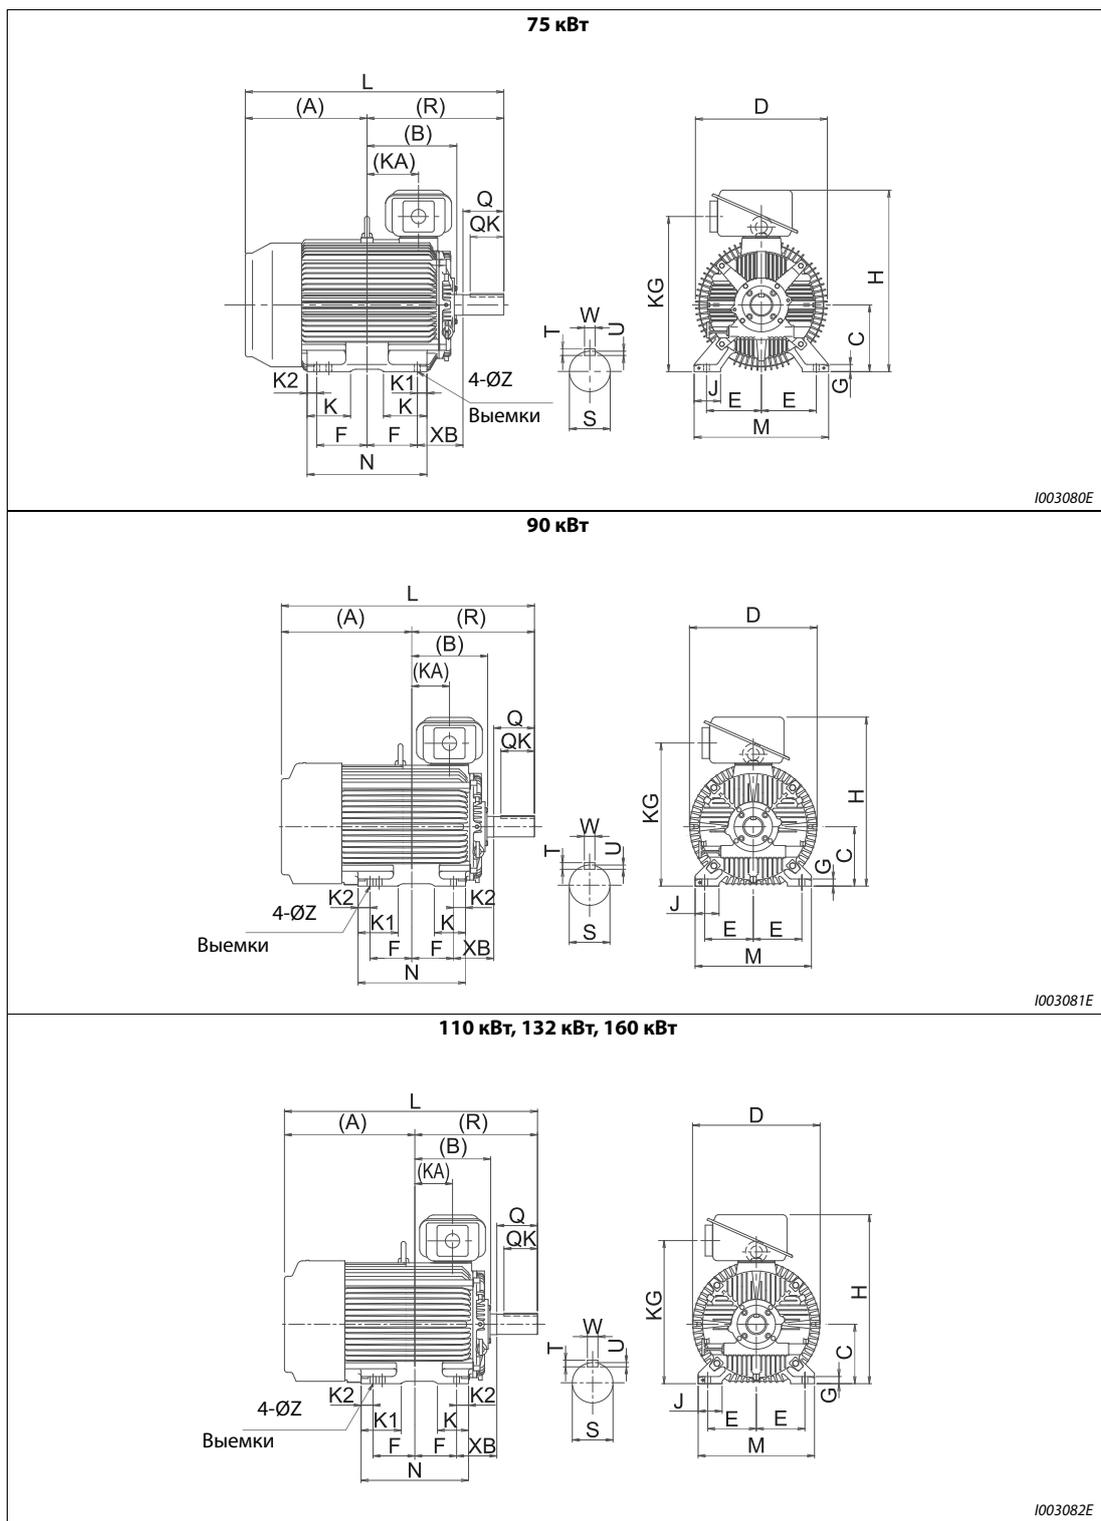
Габаритно-присоединительные размеры MM-THE4
